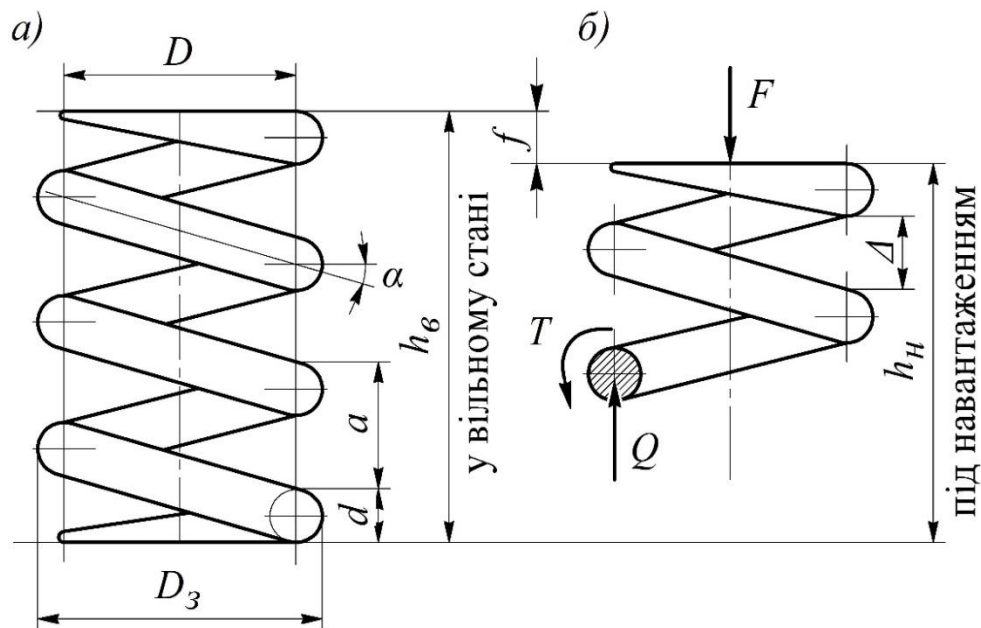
Розрахункова схема циліндричної гвинтової пружини
